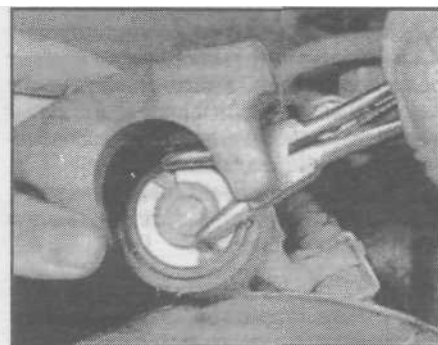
, б. Установка поршня в суппорт при помощи пассатижей для снятия стопорных колец
